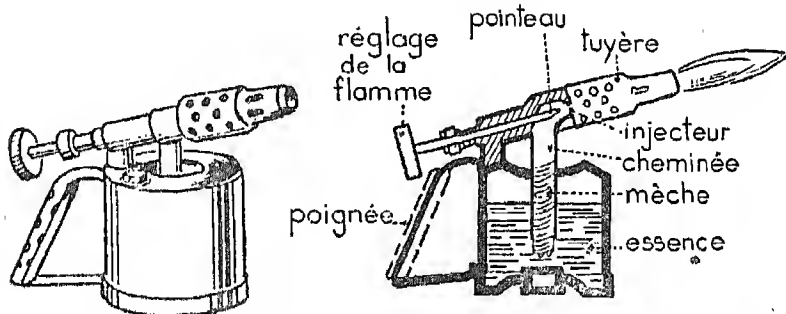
Lampe à souder. A gauche, vue d'ensemble. A droite, coupe montrant l'intérieur de la lampe.
